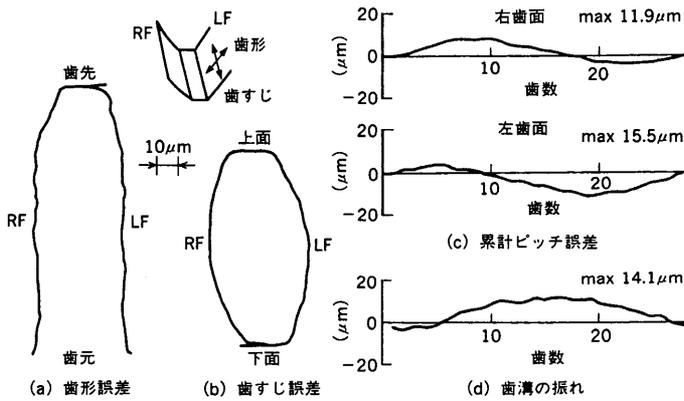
加工精度 トラック用歯車を加工した結果, JIS 1級を満足した。Machining accuracy
